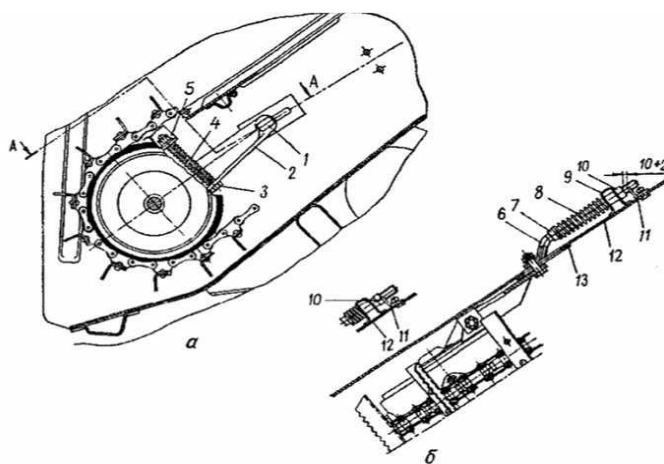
Подвеска ведомого вала транспортера наклонной камеры:
